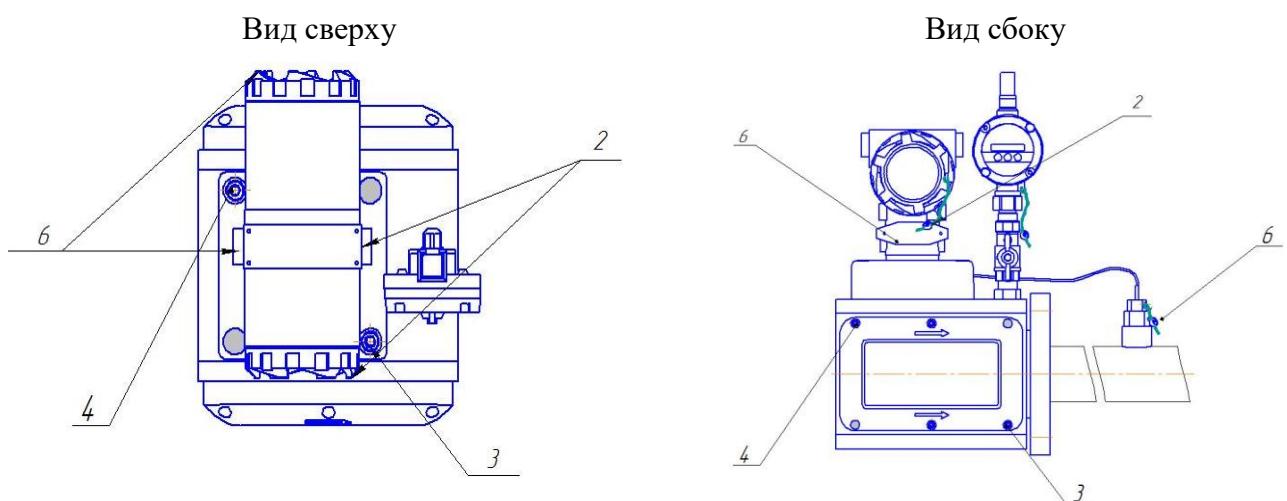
Корпус прямоугольного сечения с совмещенными защитными крышками
